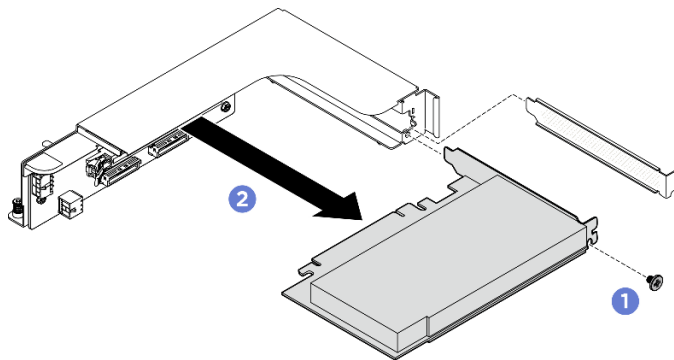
Entfernen des hinteren PCIe-Adapters
